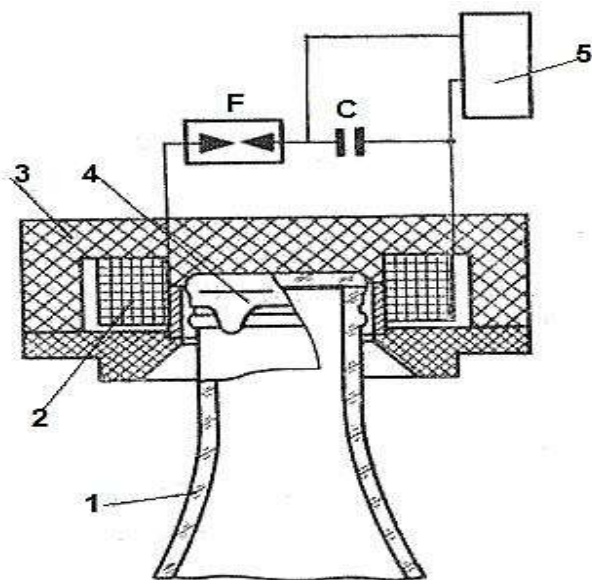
Принципова схема магнітно-імпульсного закупорювального пристрою: 1 - пляшка; 2 - індуктор; 3 -
